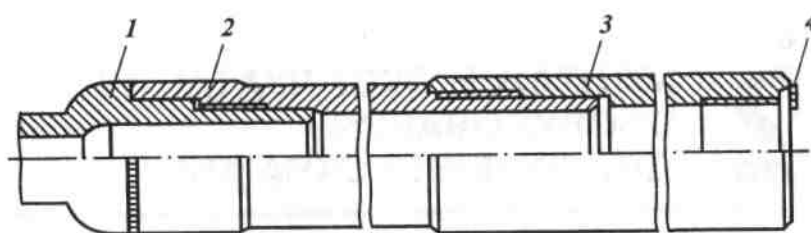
Восстановление нижней резьбы корпуса турбобура способом замены части детали: 1 - переводник; 2 - корпус турбобура; 3 - надставка к корпусу; 4 - упорная планка
